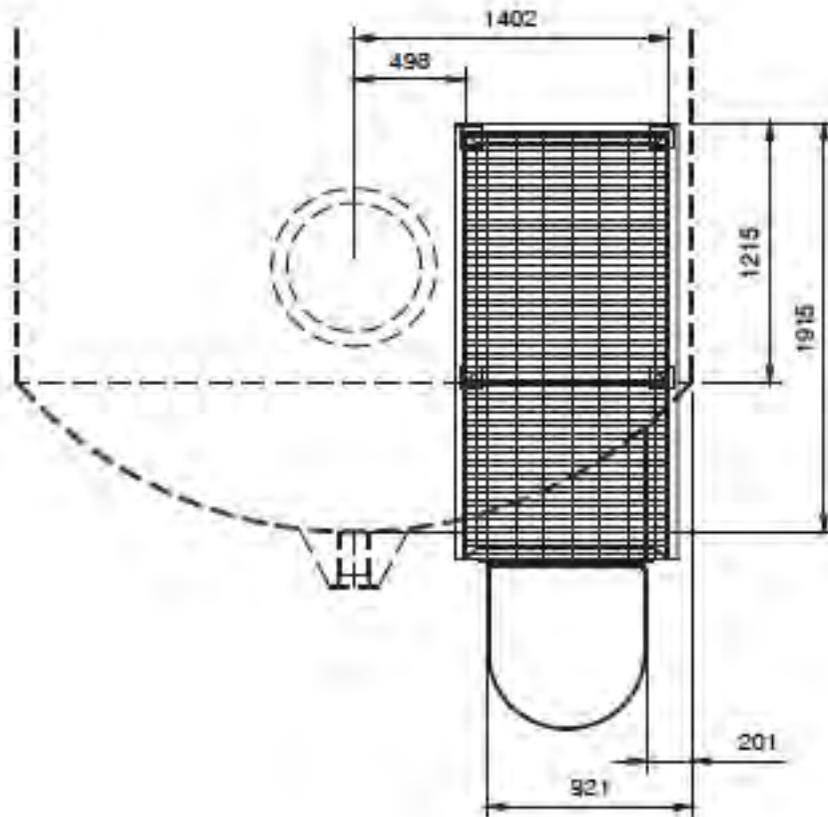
Conjunto plataforma escalera. Fuente: Planimetría Ecova
